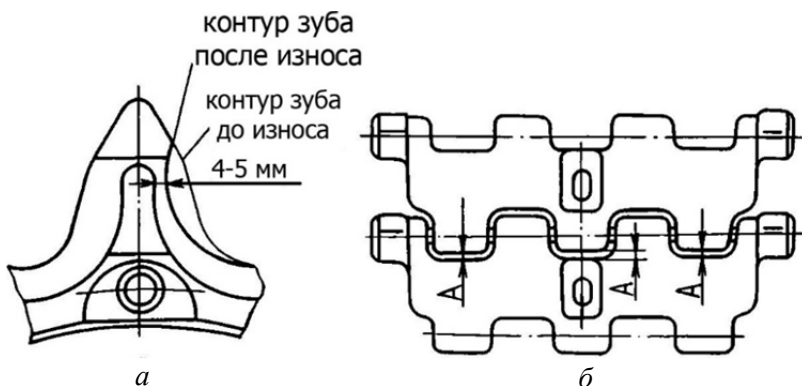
Определение износа зубьев ведущего колеса и резинометаллических шарниров гусеницы:
